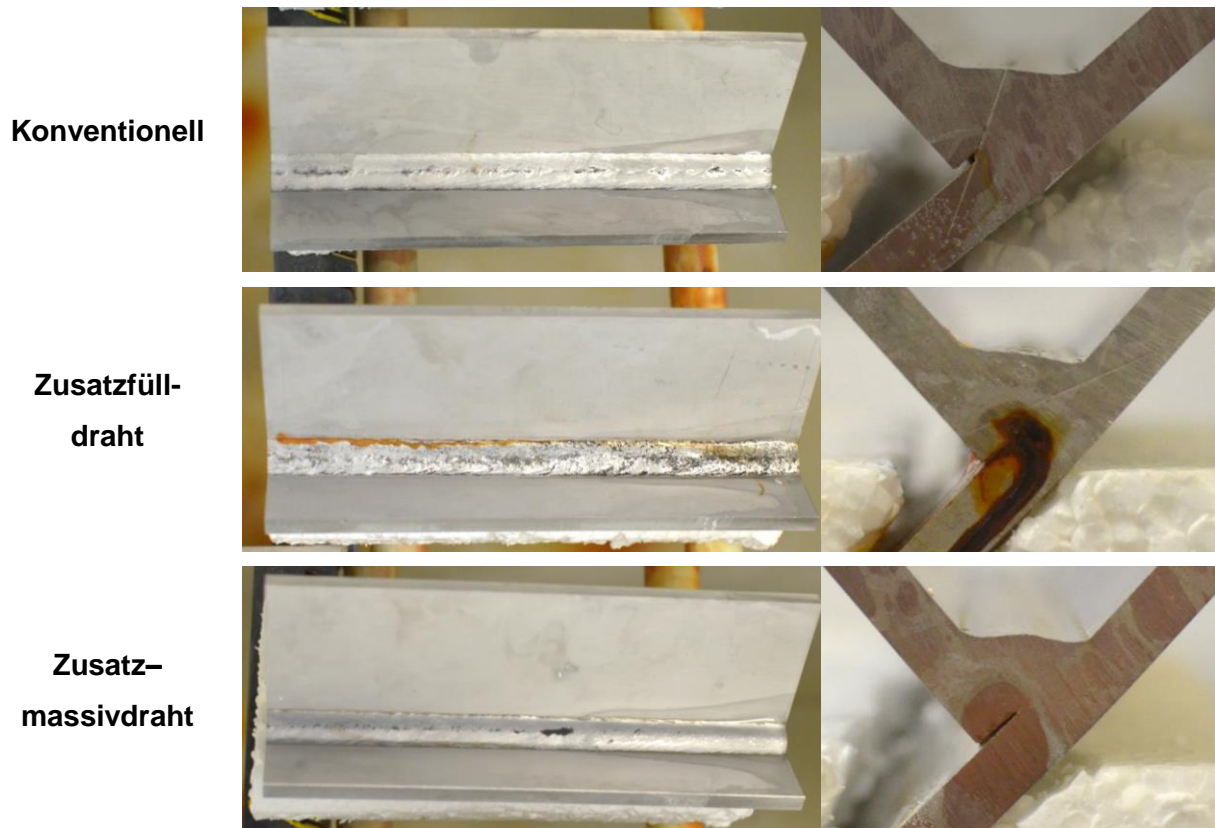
Korrosiver Angriff auf der Schweißnaht- sowie Querschnittsoberfläche nach 504 h Salzsprühstest
